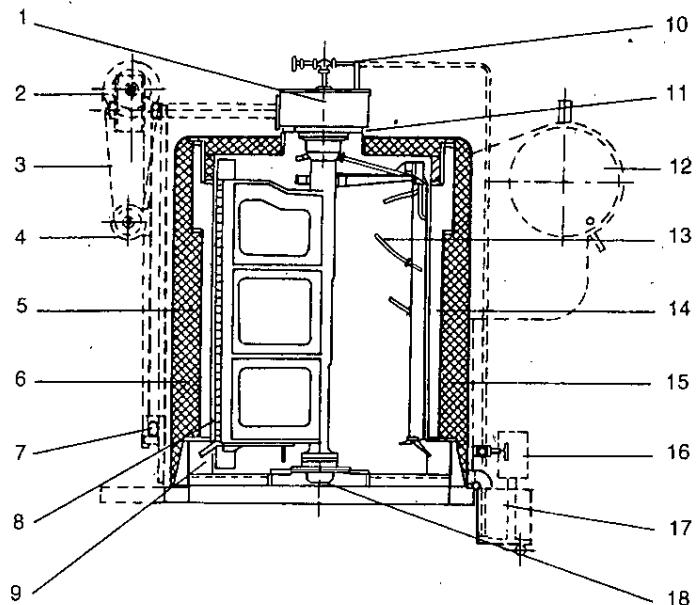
Máy làm đá mảnh của Short (Mỹ)
